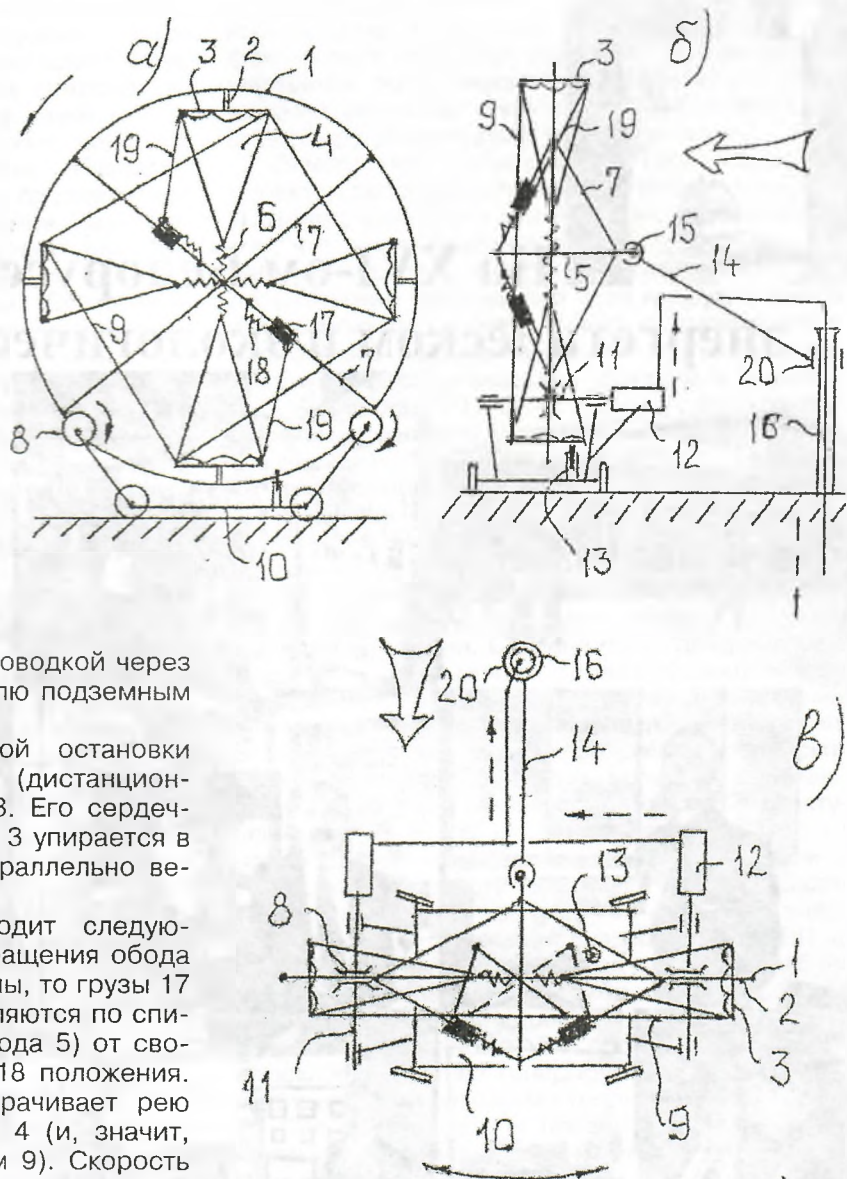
Конструкция ВЭУ "Колесо Северянина" (рей 17, 18, 19), стопор 13 и разъединяющийся упор 15.
